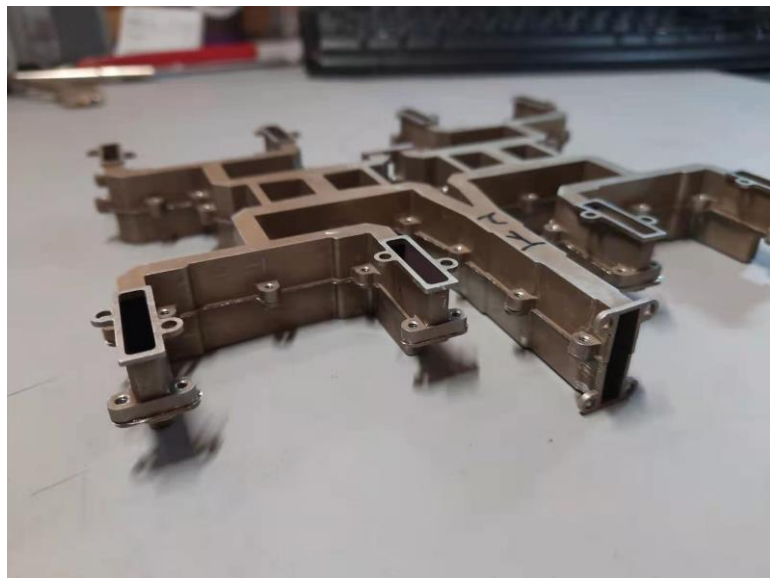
高分子纳米焊接和常规真空焊接波导进行拉力试验照片
